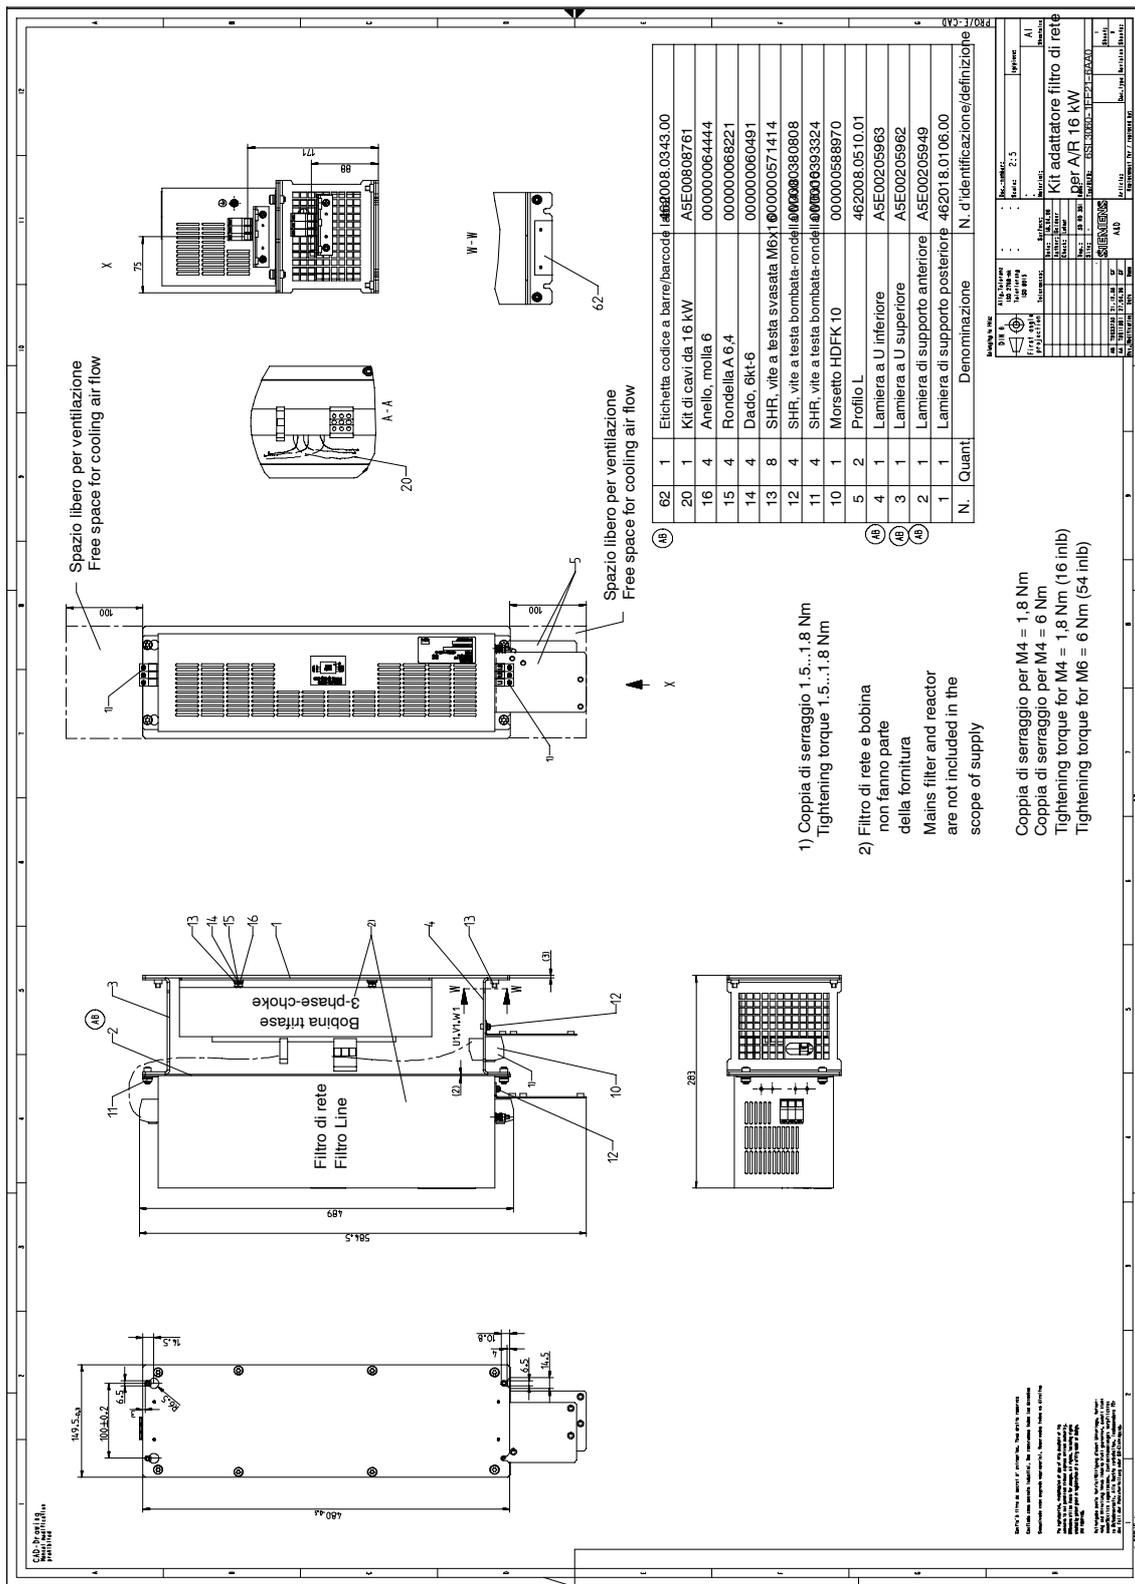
Kit adattatore filtro di rete per modulo E/R 16 kW, 6SL3060-1FE21-6AAx; disegno quotato
